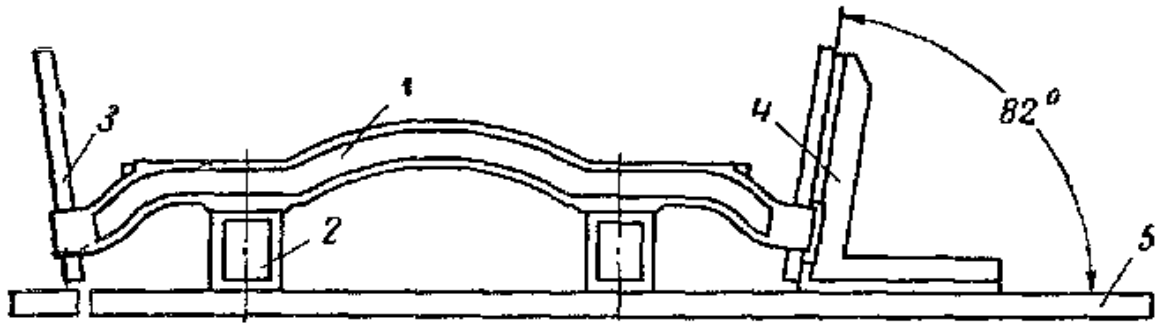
Пристосування для перевірки балки передньої вісі.
